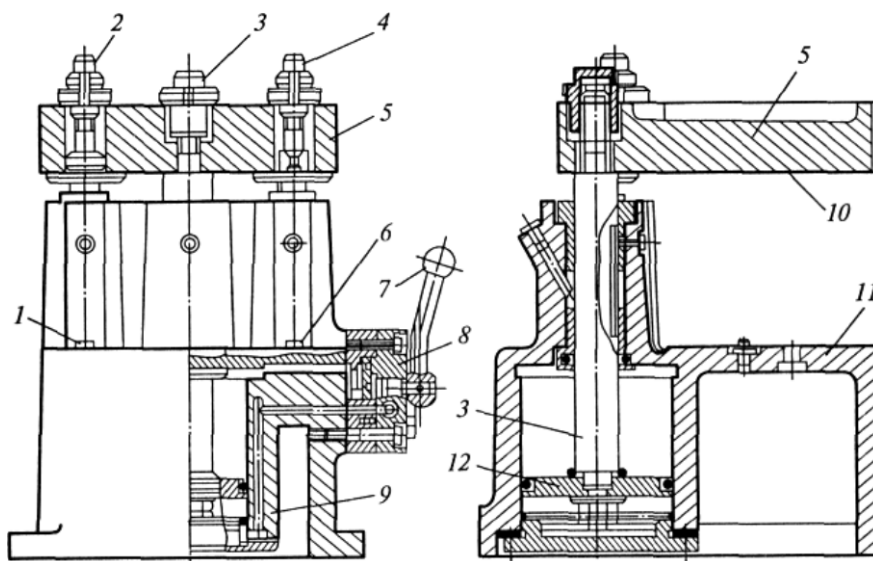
Механізований скальчатий кондуктор консольного типу з вбудованим пневмоприводом: 1, 6 – фіксуючі пальці; 2, 4 – напрямні скалки; 3 – шток поршня; 5 – постійна кондукторна плита; 7 – рукоятка; 8 – розподільний кран; 9 – пневмоциліндр; 10 – нижня площина постійної кондукторної плити; 11 – стіл корпусу пристосування; 12 – поршень
